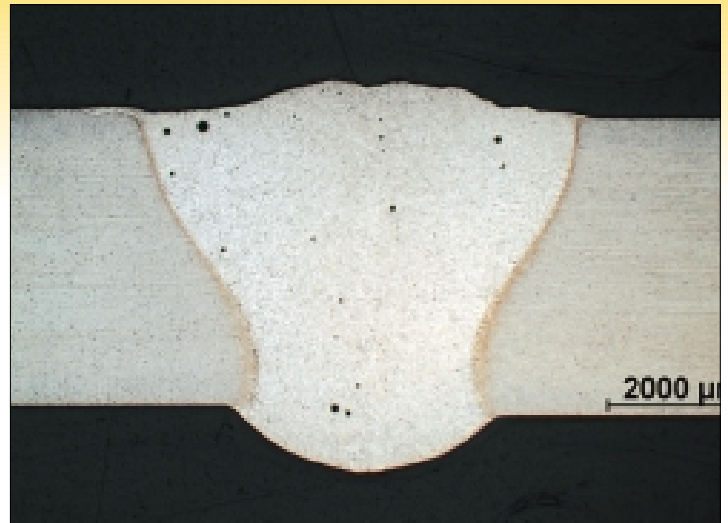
Macrographie d'une soudure hybride dans le 6082-T6. Les porosités sont nettement faibles. La vitesse de soudage est de 2,4 m/min et on a utilisé un métal d'apport 4043
